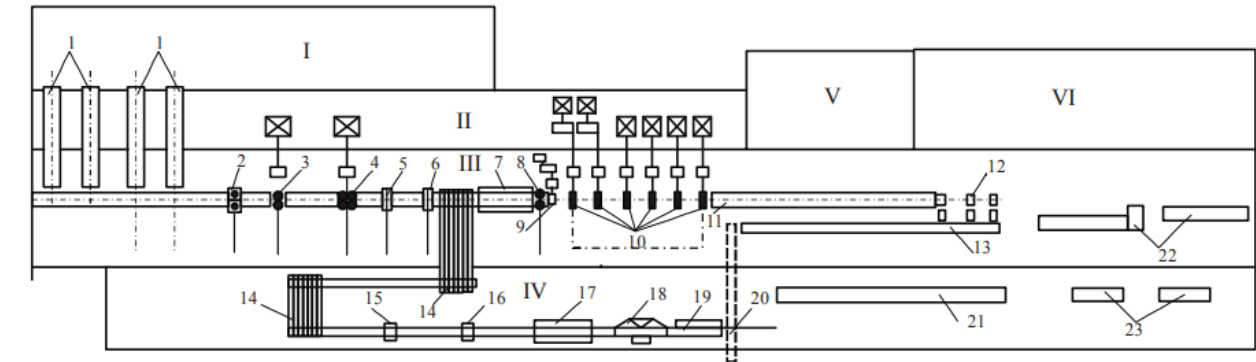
План розміщення устаткування комбінованого напівбезперервного широкоштабового стана 2300/1700: I – склад слябів; II – проліт стана; III – проліт обробки товстолистого прокату; IV – склад готової продукції; V – майстерня; 1 – нагрівальні печі; 2 – вертикальний окалиновідламувач; 3 – чорнова розширювальна кліть дуо 1100 x 2300 мм; 4 - універсальна кліть кварто 750/1400 x 2300 мм; 5 - ножиці гарячого різання; 6 - пересувна роликів правильна машина; 7 – підігрівальна роликів піч; 8 – летучі ножиці для обрізання кінців штаби; 9 – чистовий окалиновідламувач дуо; 10 – чистові кліті кварто 700/1400x1700 мм безперервної групи; 11 – відповідний рольганг; 12 – моталки; 13 – транспортер рулонів від моталок; 14 – транспортери-холодильники товстих листів; 15 – дискові ножиці з кромко подрібнювачем; 16 – ножиці поперечного різання; 17 – листоукладач; 18 – гільйотинні ножиці; 19 – стелаж; 20 – агрегат термообробки листів; 21 – травильні машини; 22 – агрегати різання; 23 – підземний транспортер гарячих рулонів
